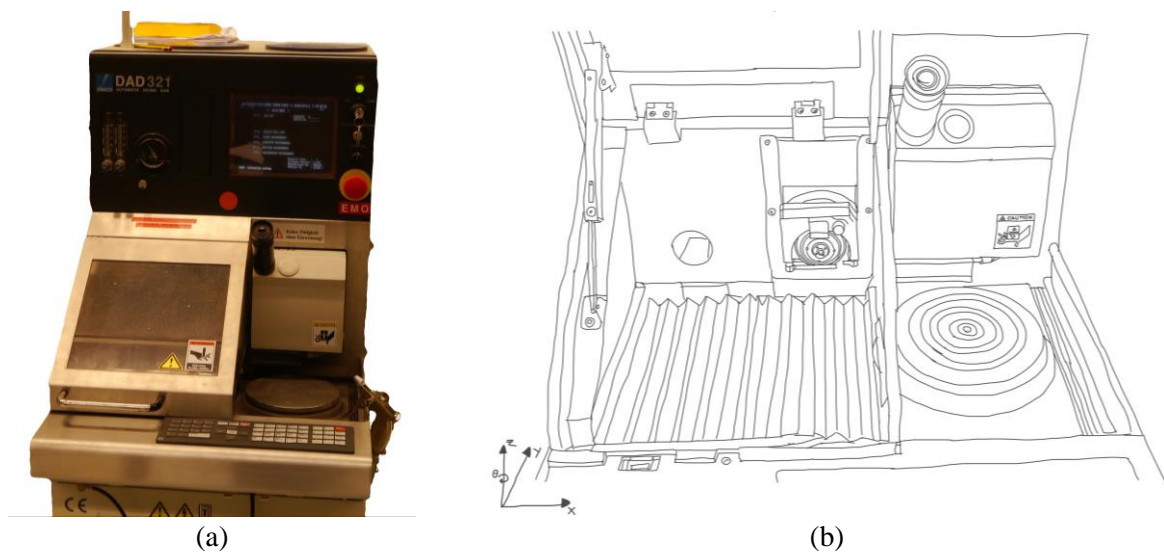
Foto der verwendeten Wafersäge DAD 321 (a). Detailzeichnung der Hauptkomponenten bei geöffnetem Bearbeitungsraum (b): Werkstückhalter (Chuck, unten rechts), Mikroskop und Spindel mit Sägeblatt.
